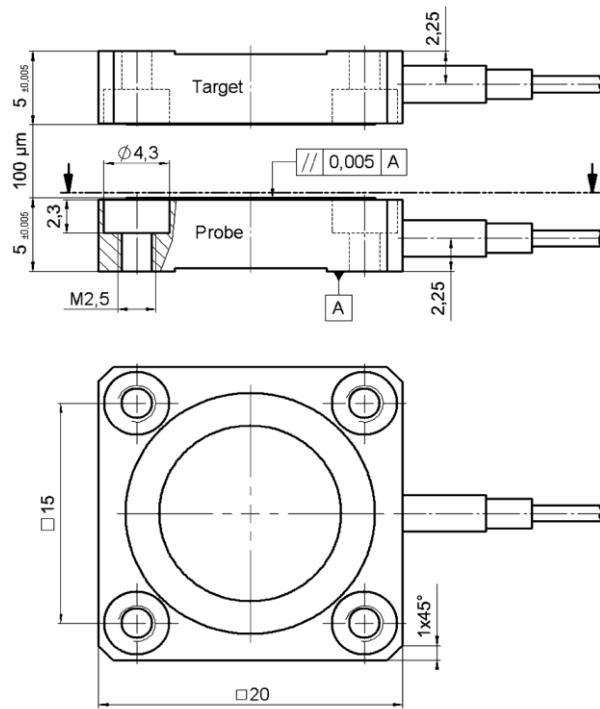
Габаритный чертёж датчика D-100.00. Размеры указаны в мм.
